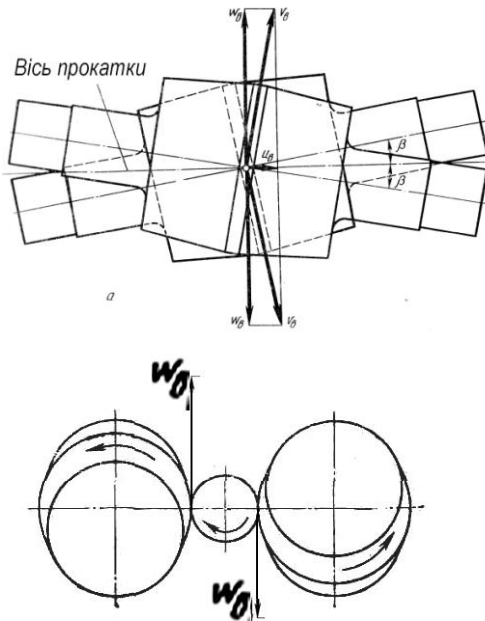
1 Схема поперечно-гвинтової прокатки у валках, розмішених під кутом до осі заготовки
